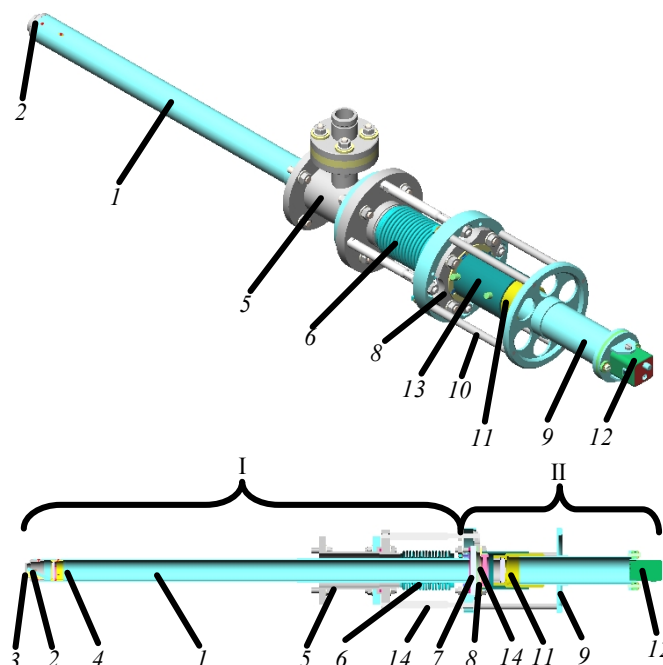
Общий вид и горизонтальный разрез эндоскопа: I — вакуумная часть; II — атмосферная часть; 1 — тубус; 2 — насадка; 3 — зрачок; 4 — линзовый объектив; 5 — переходник системы газонапуска; 6 — сильфонный узел; 7 — кварцевое окно; 8 — обойма-держатель фильтра; 9 — тубус; 10 — клетка; 11 — линзовая насадка; 12 — видеокамера; 13 — подвижный кожух; 14 — интерференционный фильтр
